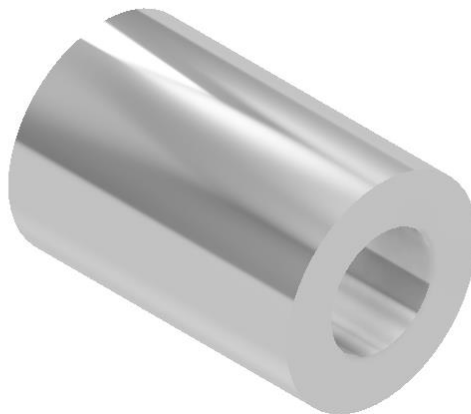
Τρισδιάστατη απεικόνιση αποστολής 56
